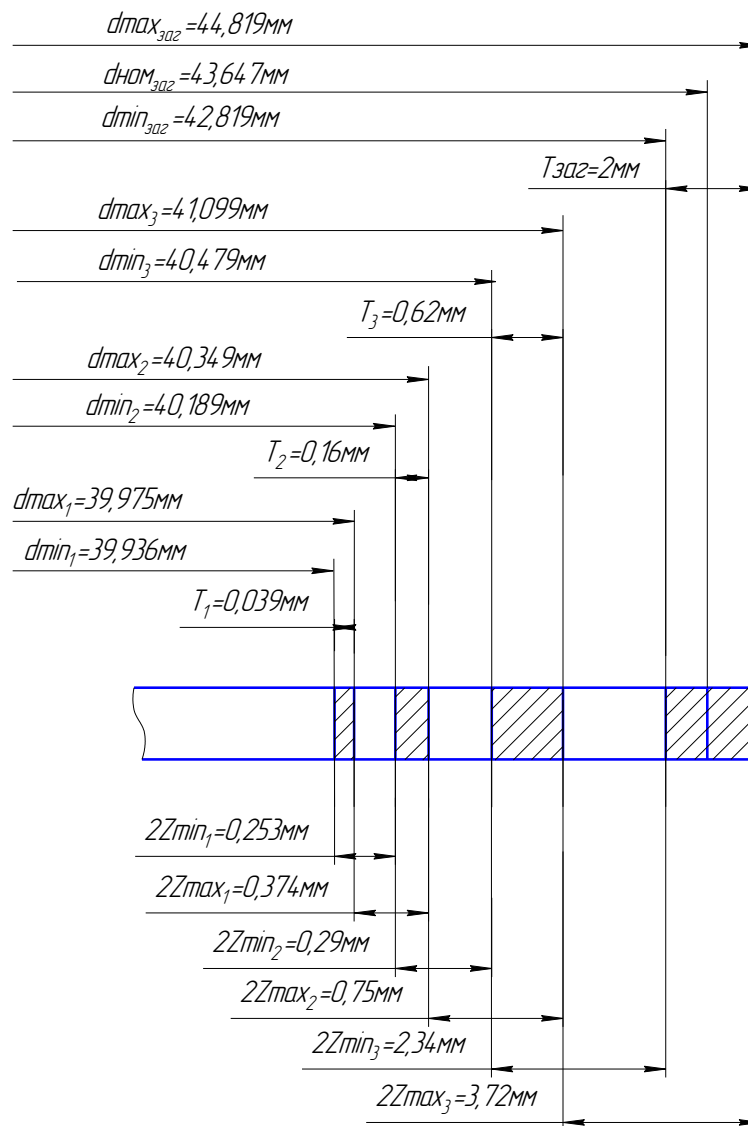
Схема розміщення допусків і припусків на обробку поверхні $\varnothing 40f8^{(-0,025)}_{(-0,064)}$
